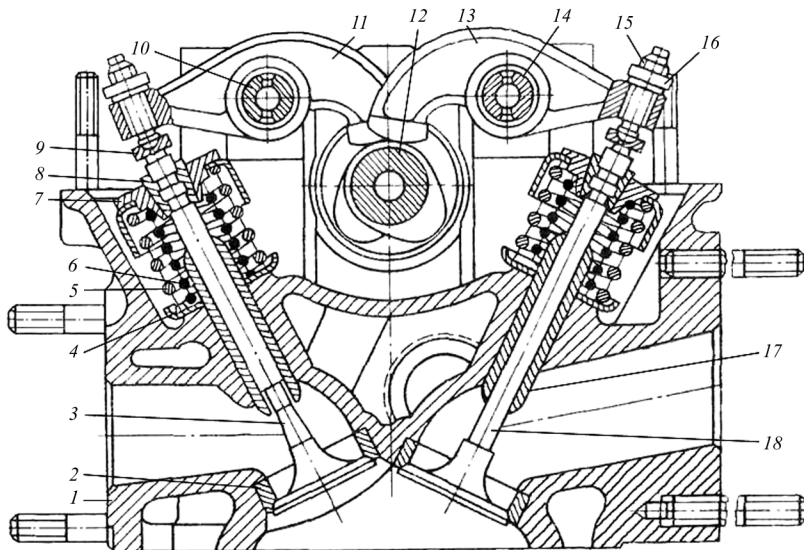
Расположение деталей клапанной группы ГРМ с приводом с помощью коромысел: 1 – головка блока цилиндров; 2 – седло клапана; 3 – впускной клапан; 4 – опорная тарелка пружин клапана; 5 – пружина клапана внешняя (большая); 6 – пружина клапана внутренняя (малая); 7 – тарелка пружин клапана; 8 – сухарь; 9 – наконечник клапана; 10, 14 – ось коромысел; 11, 13 – коромысло; 12 – распределительный вал; 15 – регулировочный винт; 16 – контргайка; 17 – направляющая втулка клапана; 18 – выпускной клапан
